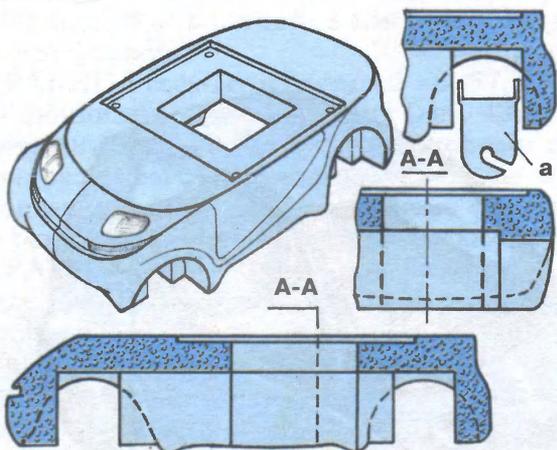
Деталь нижней части кузова: а — скоба крепления ведущего моста.
